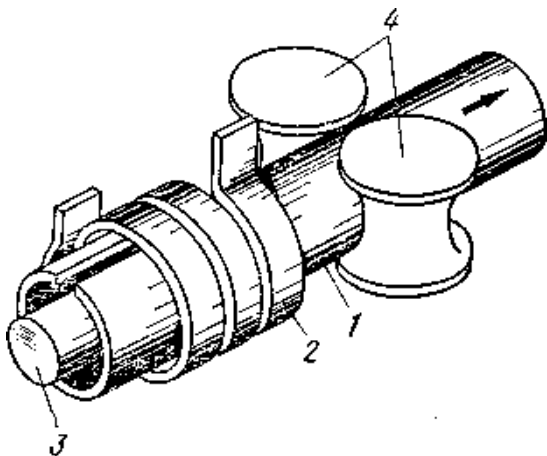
Схема процесу індукційного зварювання труб: 1 – труба; 2 – індуктор, 3 – осердя; 4 – обтискові ролики
